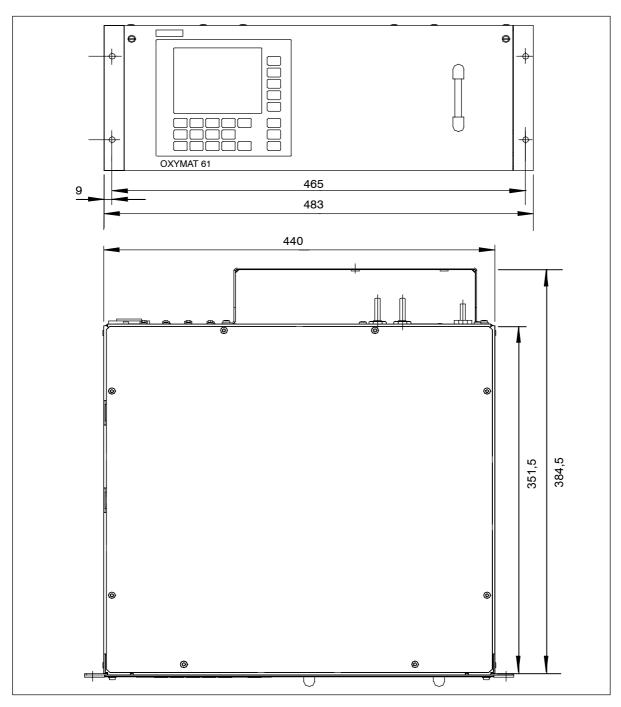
Maße zur Installationsvorbereitung (Vorderansicht und Draufsicht)
